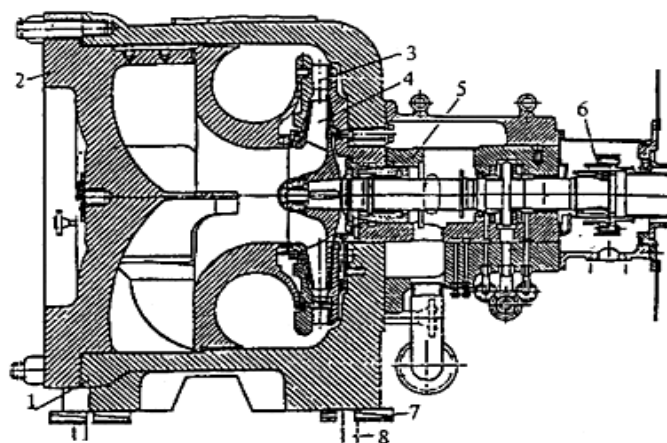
Неполюнапорный одноступенчатый нагнетатель 370-18
